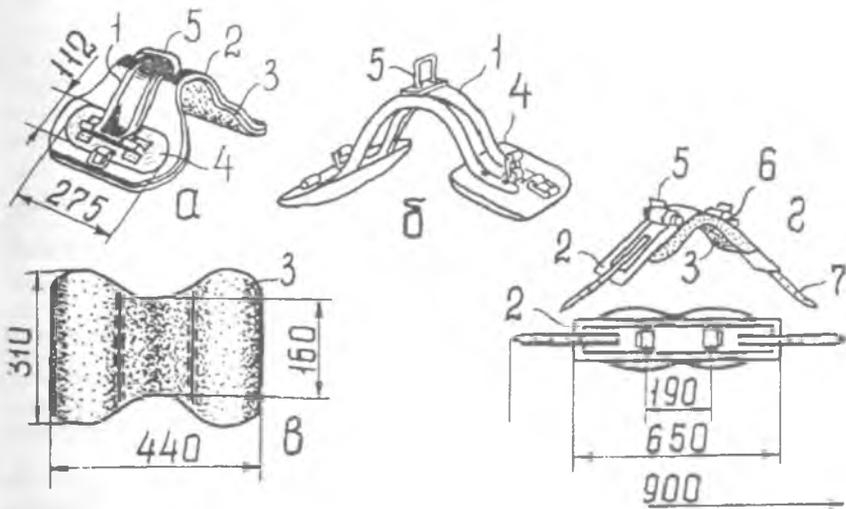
Седелки: а - горбатая седелка с качающимися металлическими полками; б - горбатая седелка с неподвижными деревянными полками; в - войлочная подушка для горбатой седелки; г - прямая седелка. 1 - арка стальная; 2 - покрывка; 3 - войлочная подушка; 4 - полка; 5 - дужка; 6 - колодки деревянные; 7 - горт сыромятный
